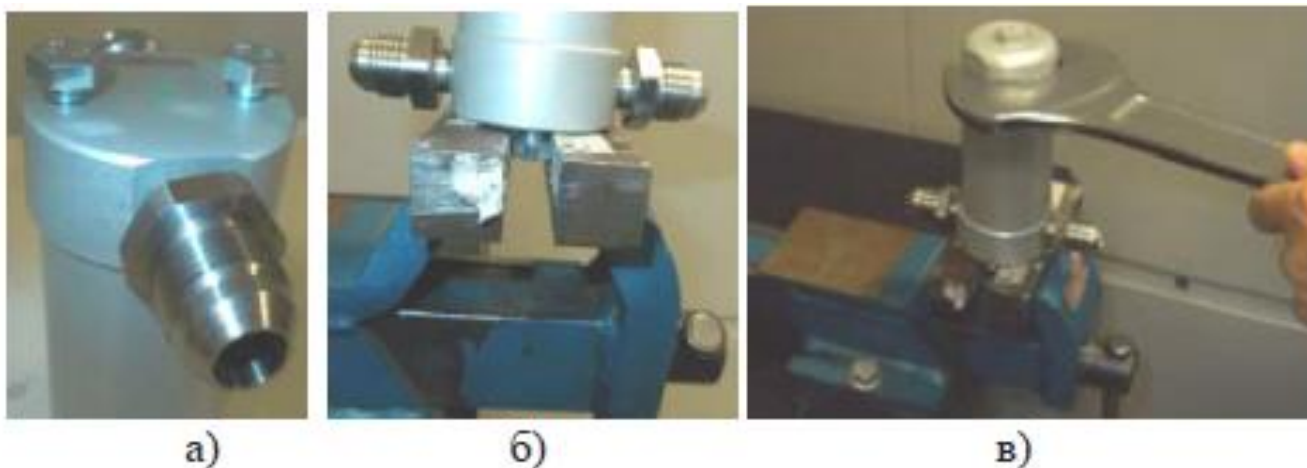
Снятие и установка корпуса фильтра высокого давления
